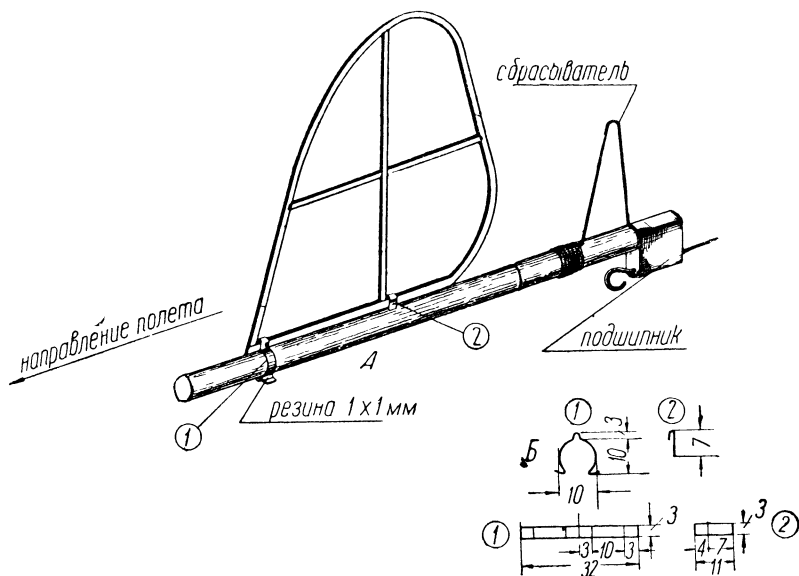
Крепление киля: А — общий вид крепления; Б — детали крепления и их развертки
